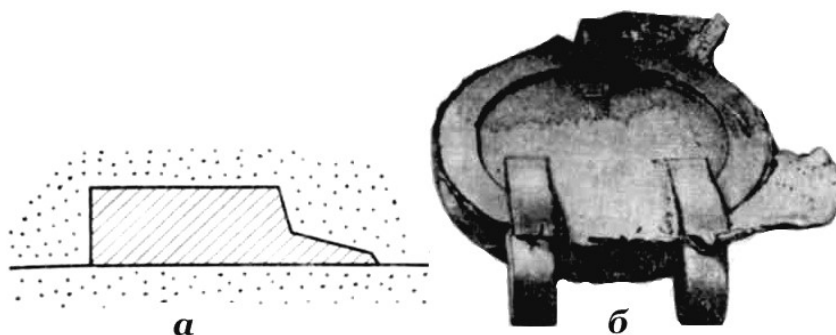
Залив: а – схема; б – дефектная отливка
